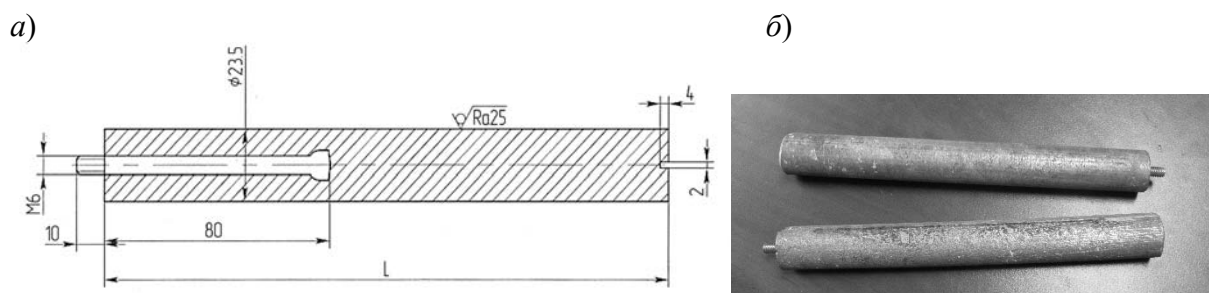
Изделие «протектор» из магниевого сплава: а – чертеж детали «протектор»; б – образцы отливок
